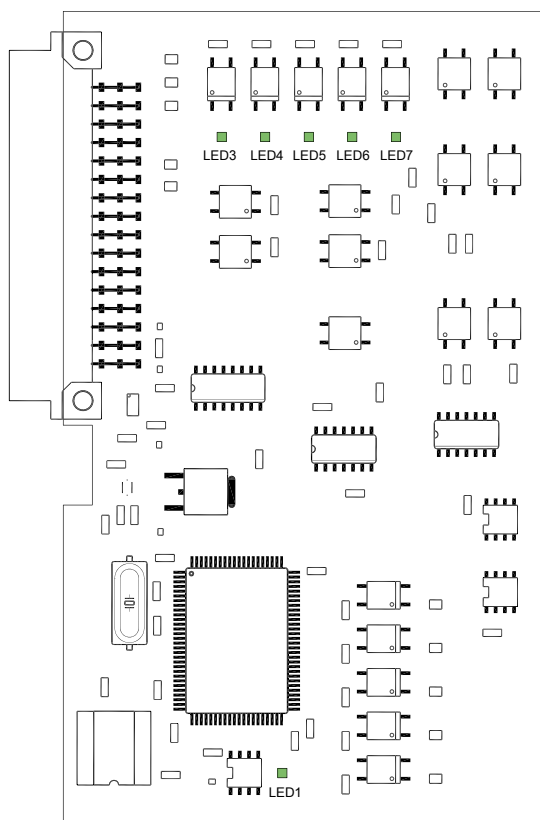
ไฟLED ในการควบคุม applicator PCB
